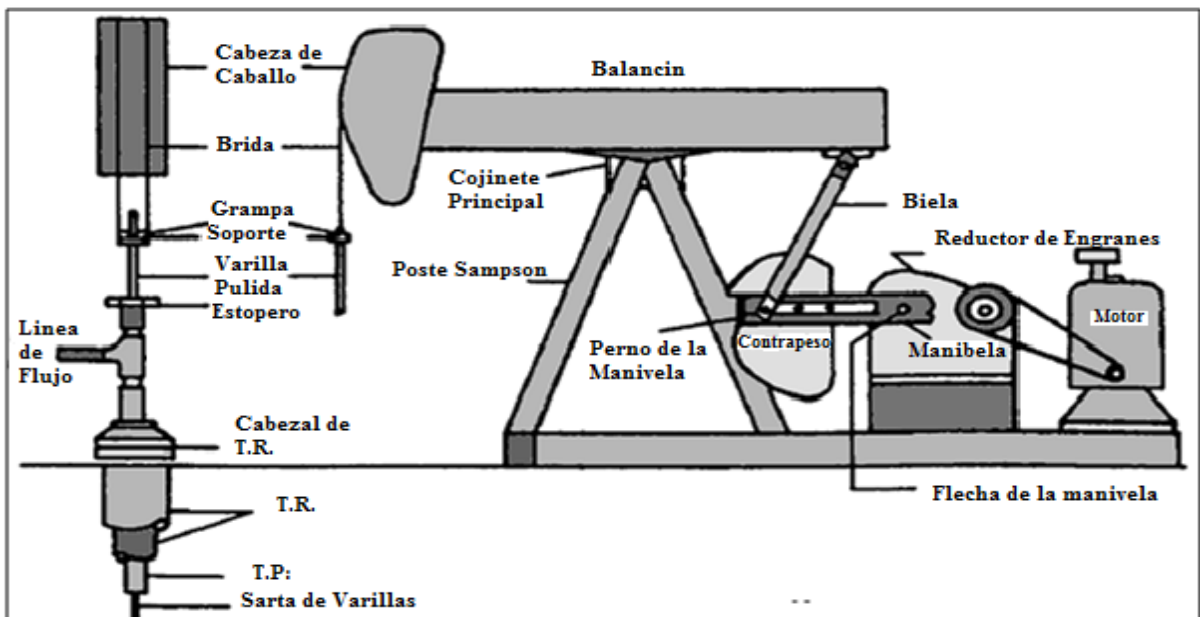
Componentes de Unidad de Bombeo Mecánico tipo Balancín.
